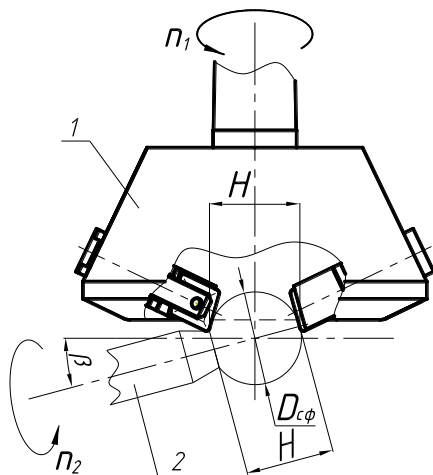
Схема обработки сферической поверхности способом высокоскоростного фрезерования:
